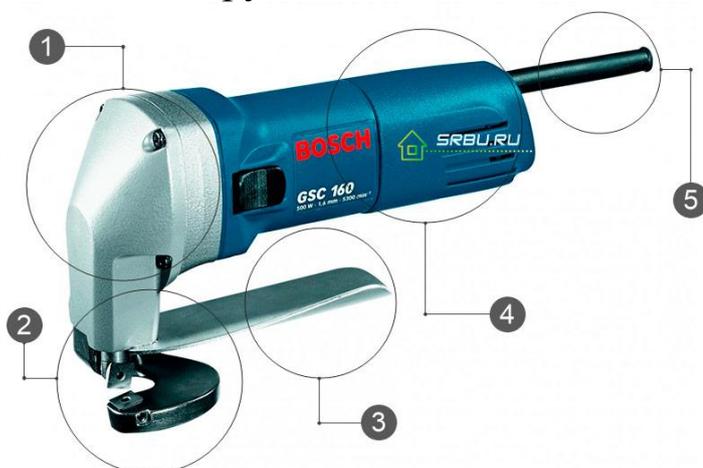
1 - многоступенчатый редуктор; 2 - рабочий узел; 3 - защитная пластина-щиток; 4 - пластиковый корпус со встроенным электрическим двигателем; 5 - электрический шнур
